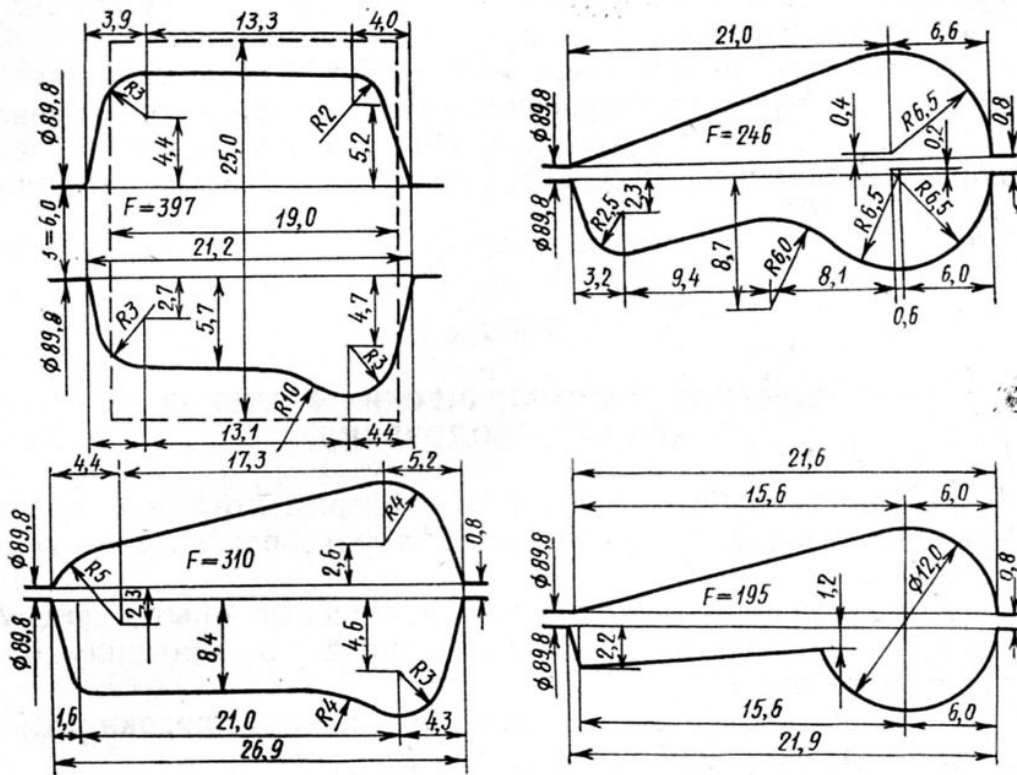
Калибровка валков для прокатки профиля «собачка» в четыре пропуска.
